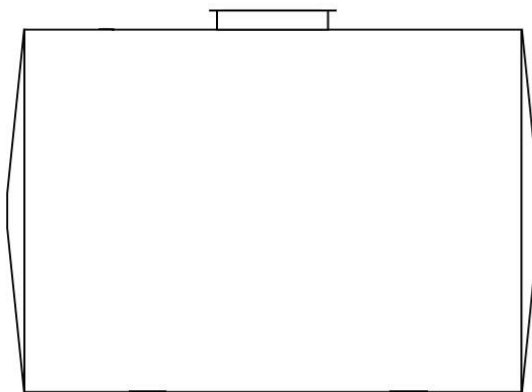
Эскиз резервуара РГС-5 зав.№ 17
